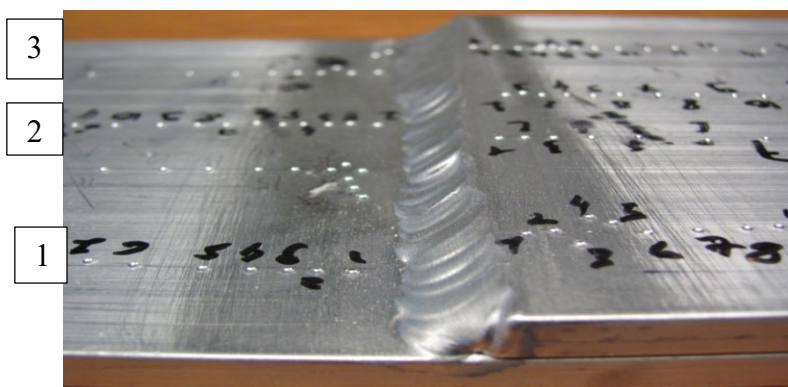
Cordon de soudure, épaisseur 6 mm
